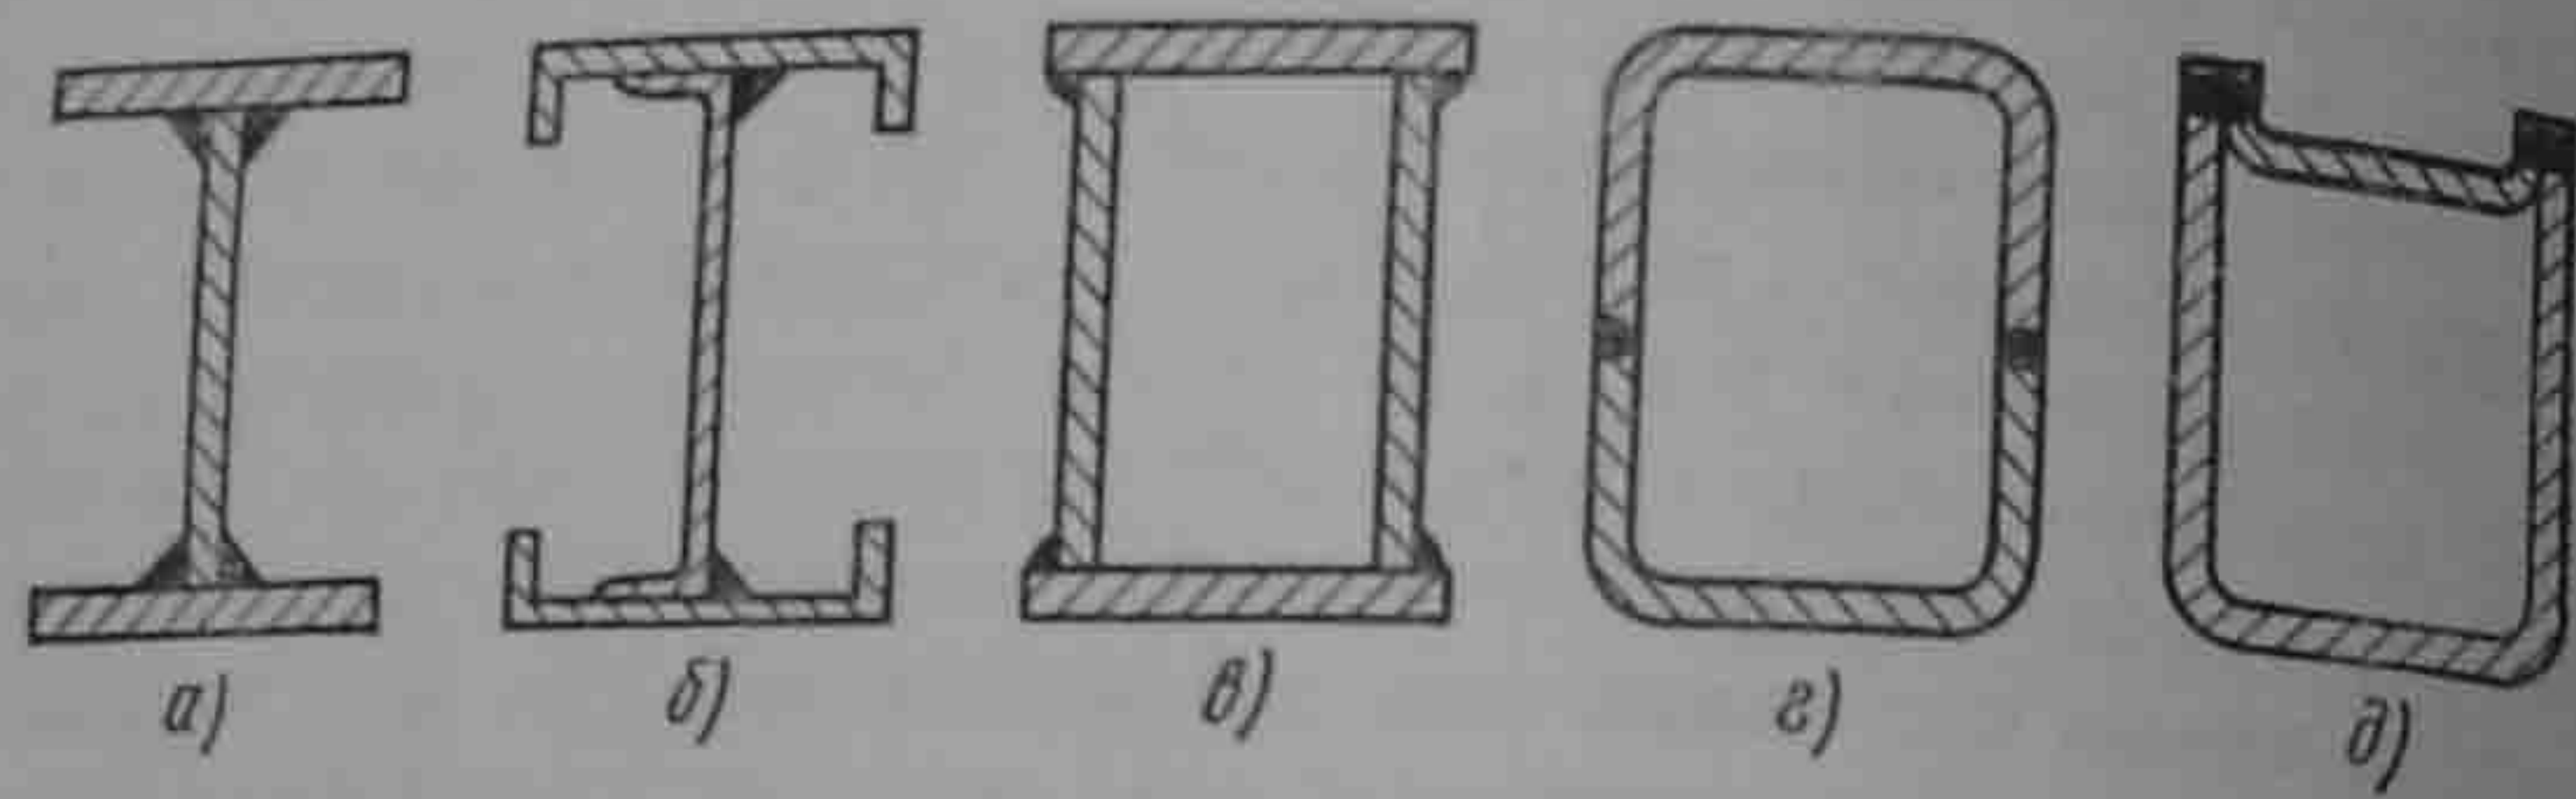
Варианты сварных двутавровых и коробчатых балок
